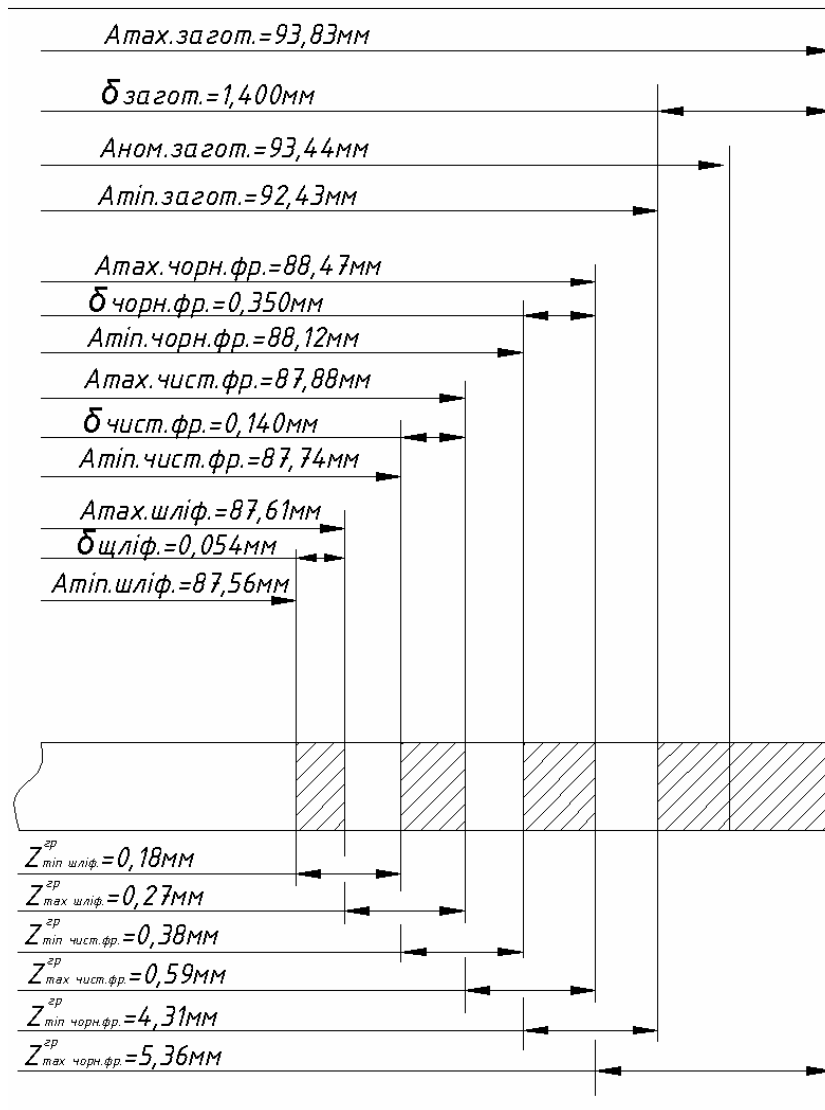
Схема графічного розташування припусків і допусків на оброблення поверхні 6.
